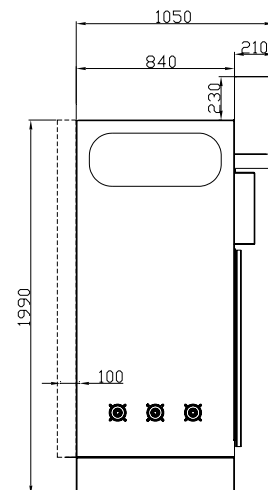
Габаритные размеры КСО с шириной корпуса 500 мм
